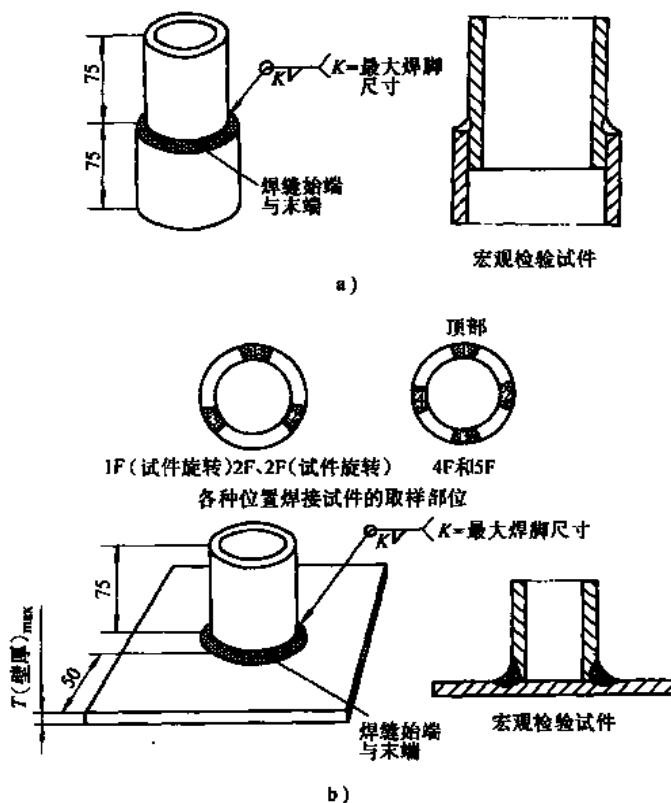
管材角焊缝焊接工艺评定试件形式和尺寸要求
